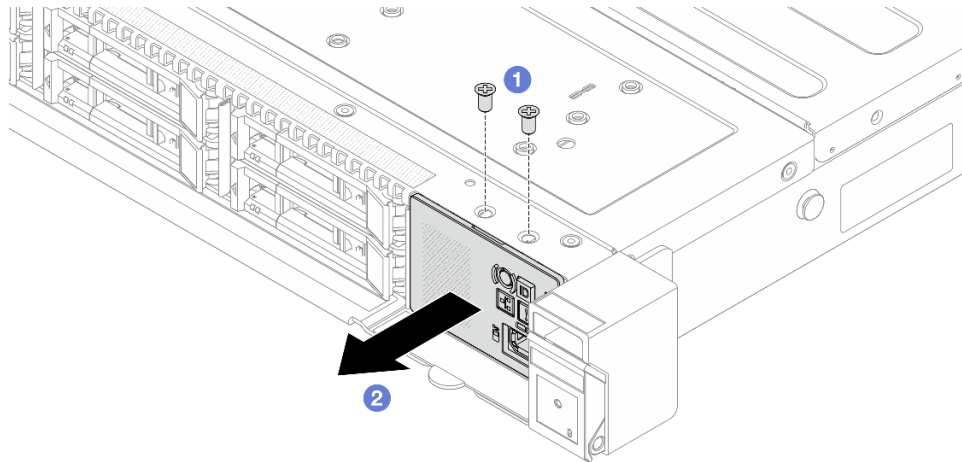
Extracción de un módulo de E/S frontal en el chasis de 2,5"
